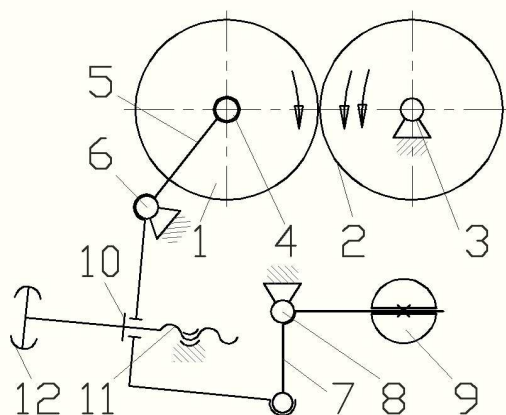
Конструкция установочного механизма с рычагом первого рода
